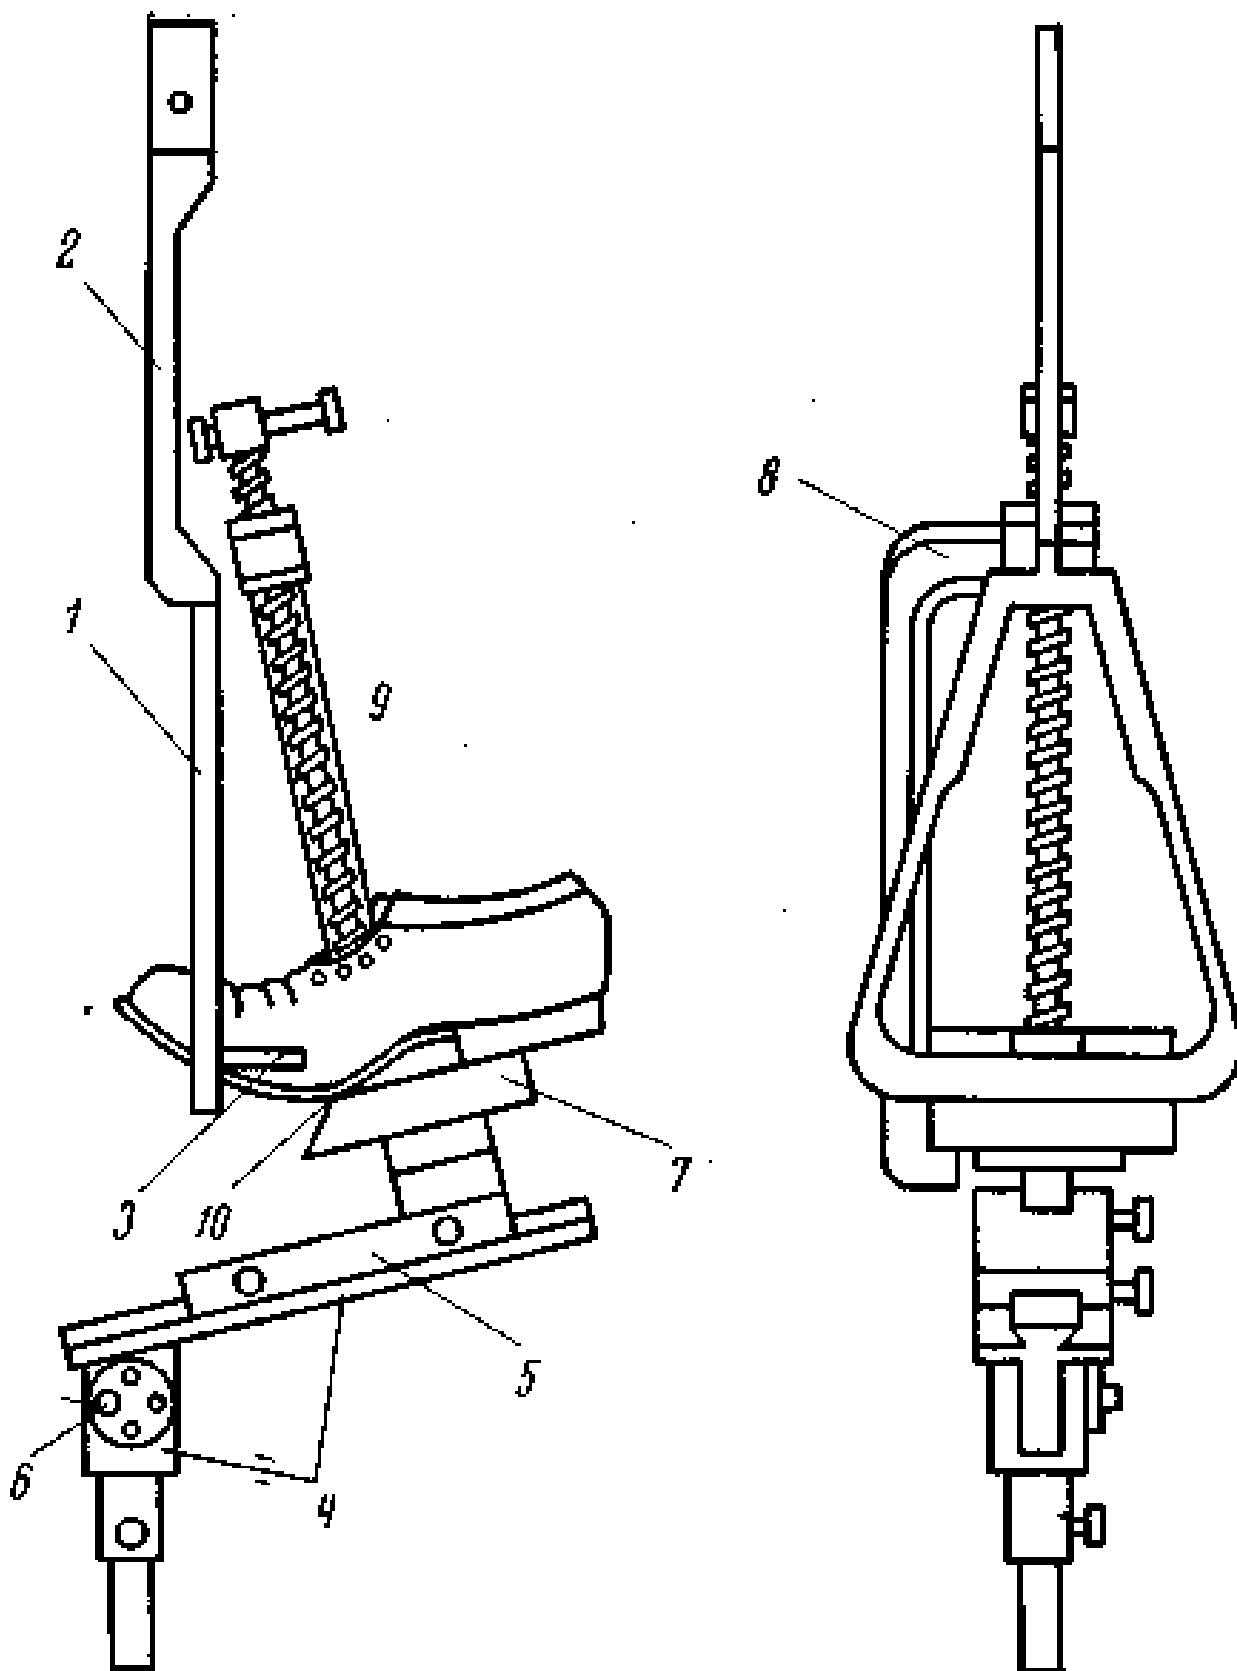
Схема приспособления к разрывной машине для определения гибкости обуви
